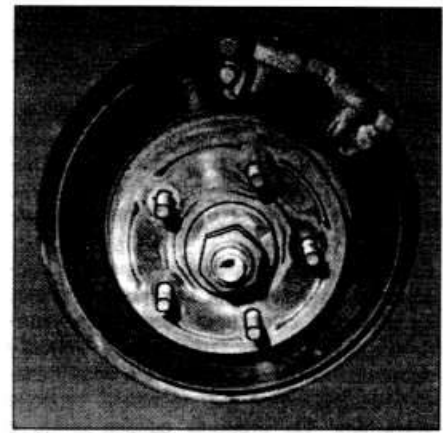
Стопорное кольцо тормозного диска заднего колеса
